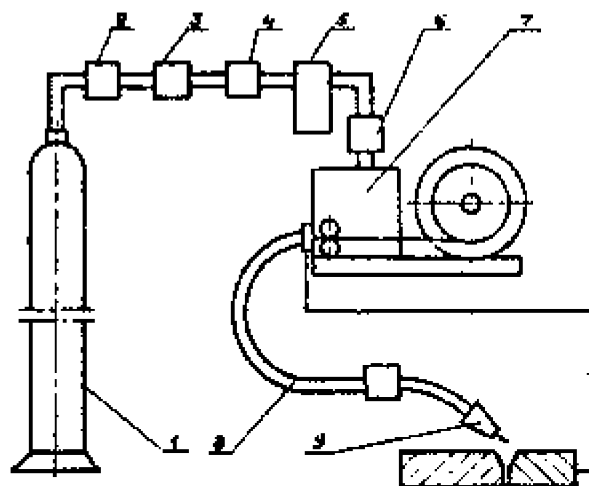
Схема установки полуавтомата для сварки в среде углекислого газа:
